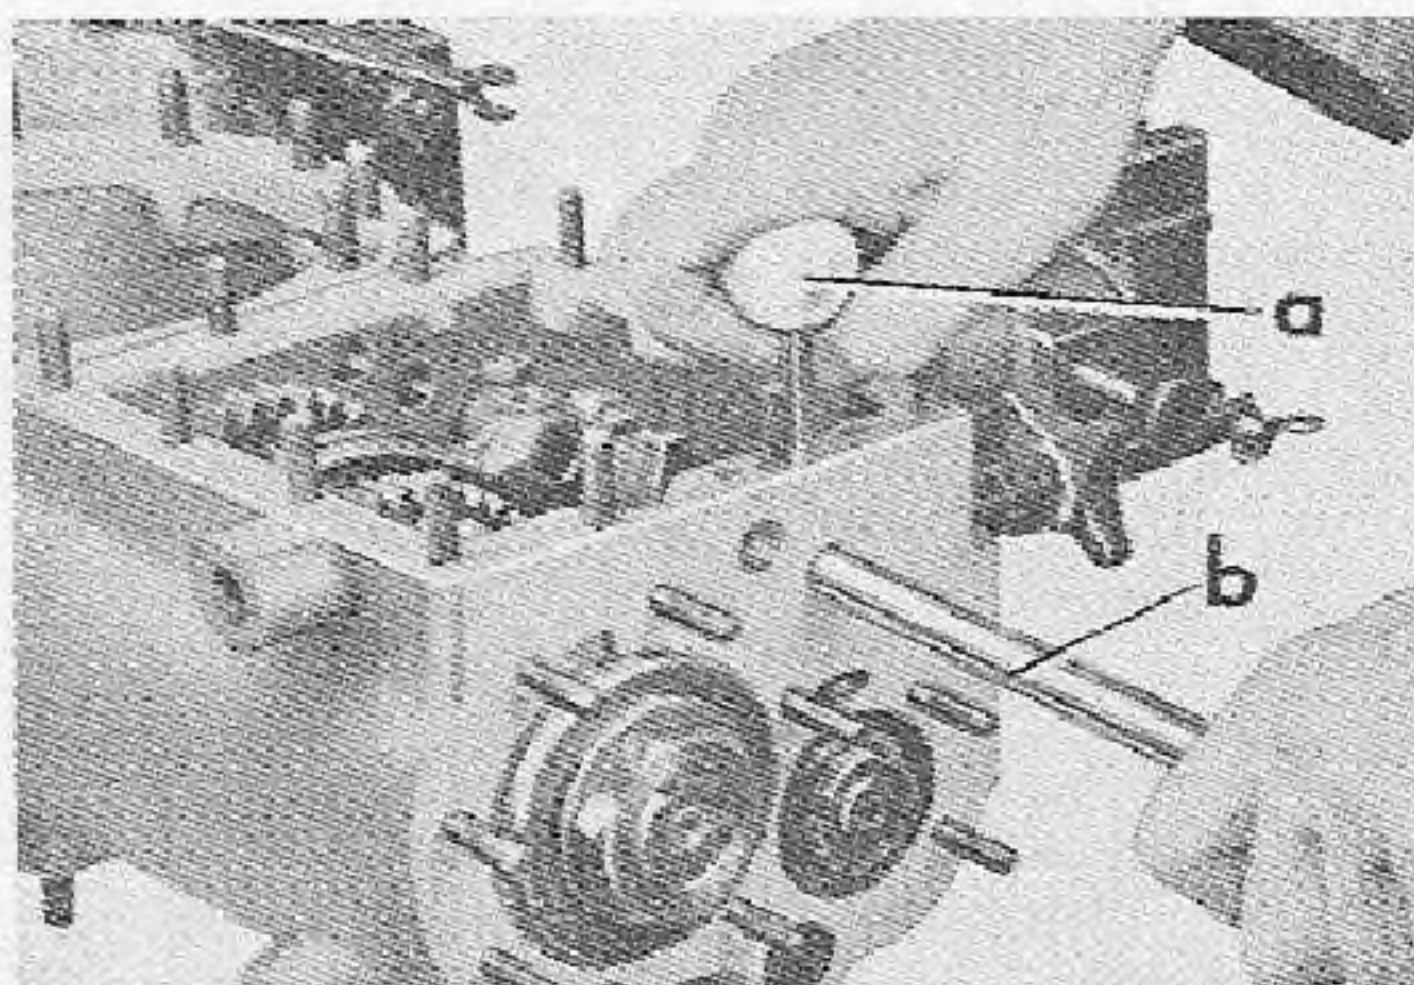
Montaje del eje de horquilla de 1ª y 2ª.
